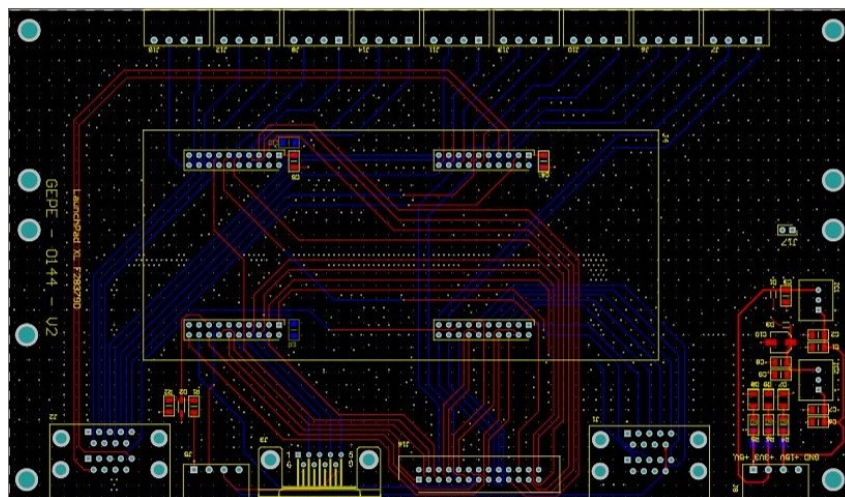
Layout* da PCB da plataforma para a DSC no Altium PCB Designer.
